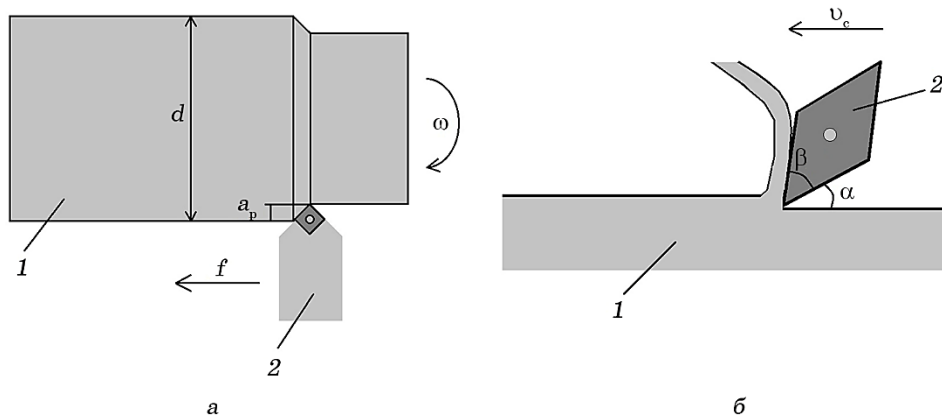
Параметри механічного оброблення заготовки з титану: 1 — заготовка з титану; 2 — різальний інструмент.
